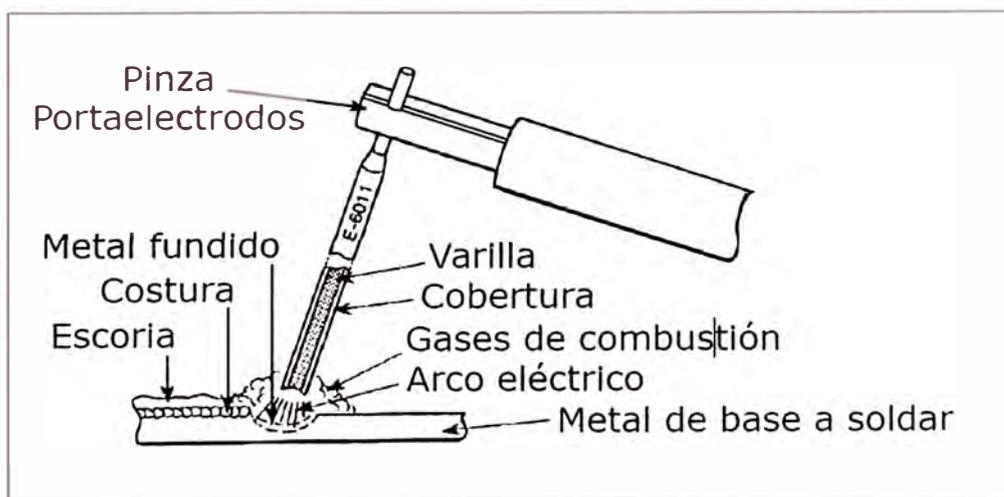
Esquema del proceso de soldadura SMAW
